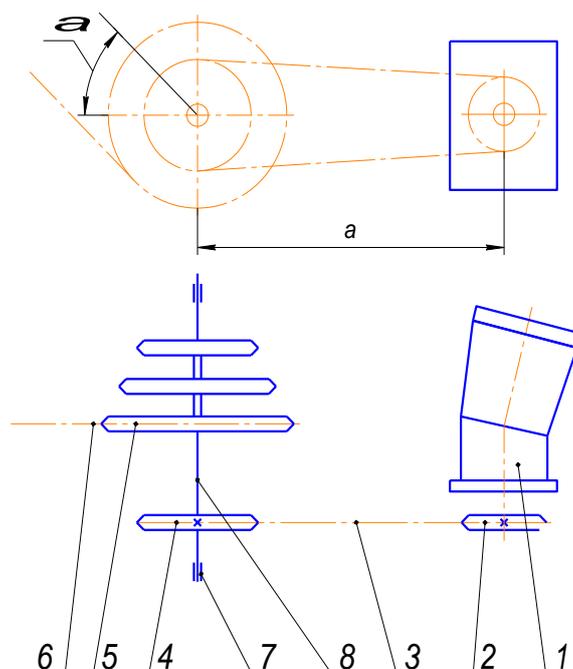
Кинематическая схема привода валов зерно- и туковысевающих аппаратов агрегата АУП-18.
